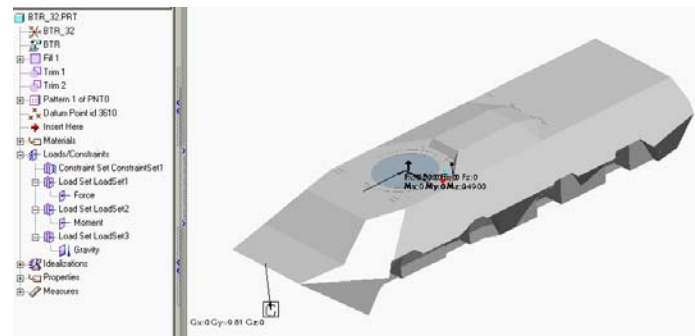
Модель корпуса БТР-80 с заданными нагрузками
